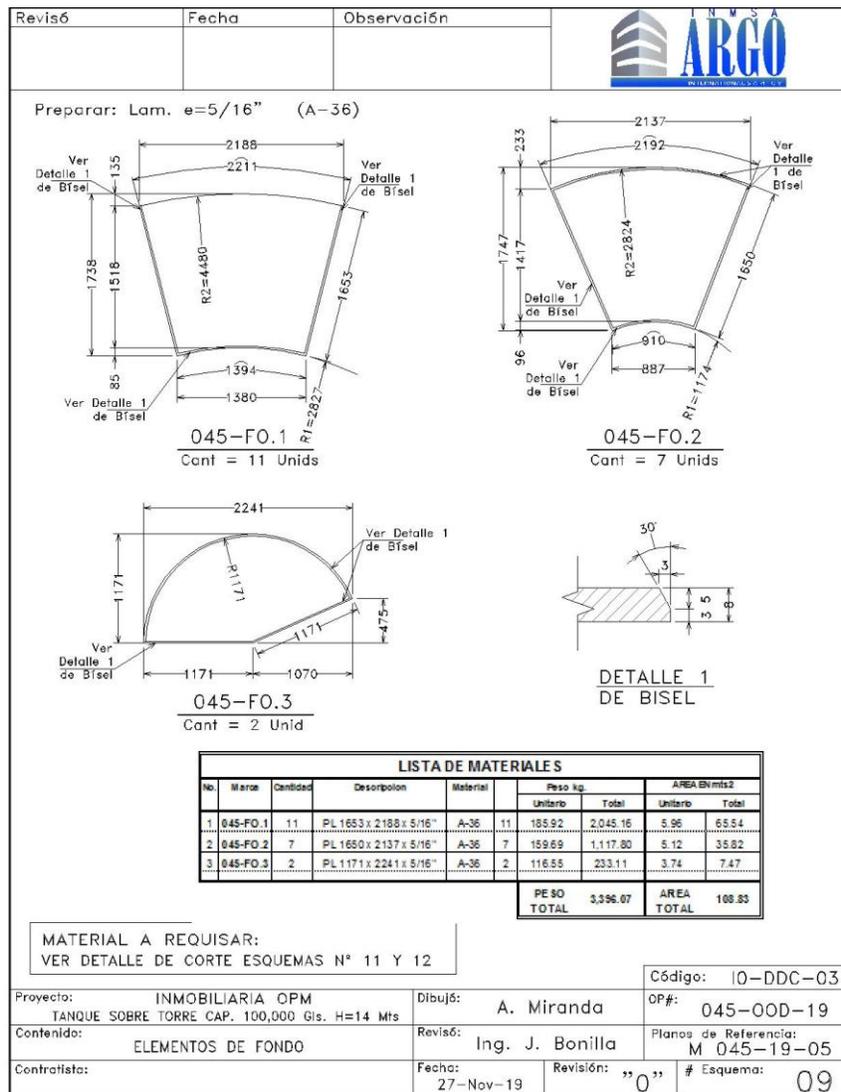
Esquema de fabricación de elementos de fondo de tanque elevado
